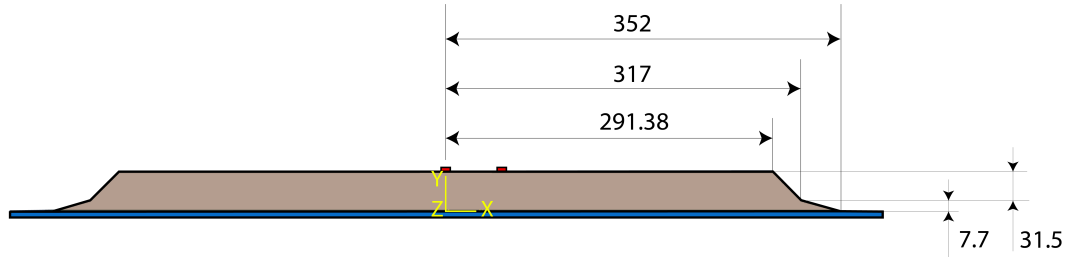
Vista de perfil con dimensiones de la probeta.
